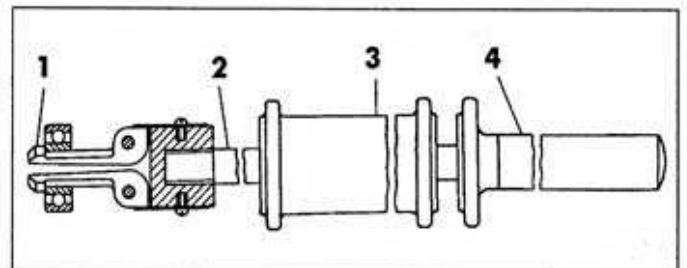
Съемник 7823-6090 для выпрессовки подшипника из коленчатого вала:
